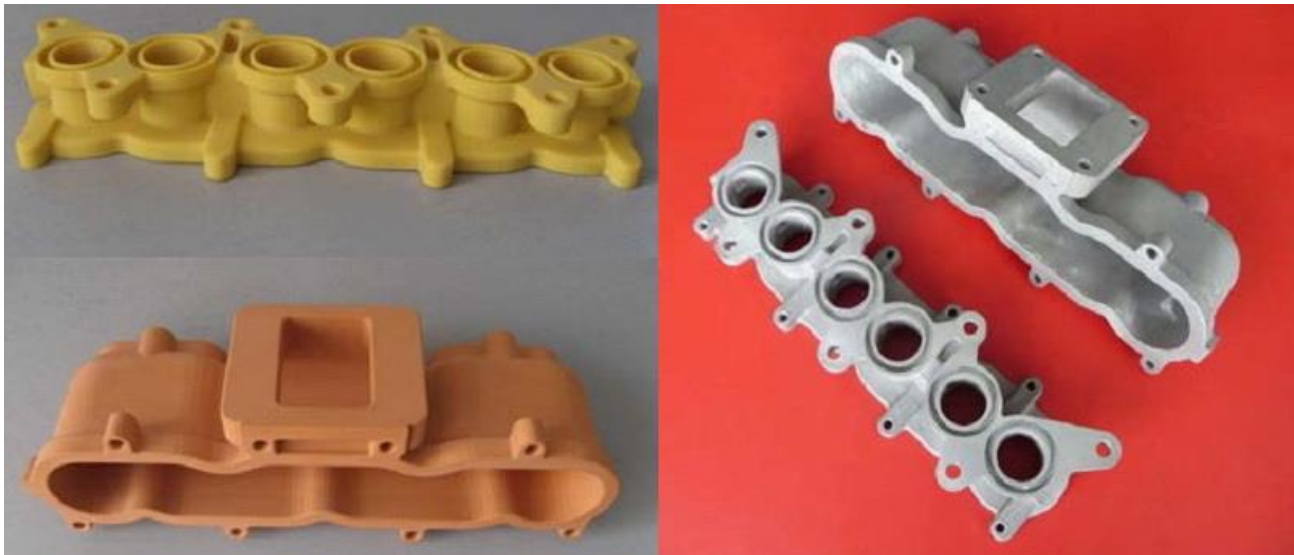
Модели Envisiontec и отливки деталей ДВС из алюминия
